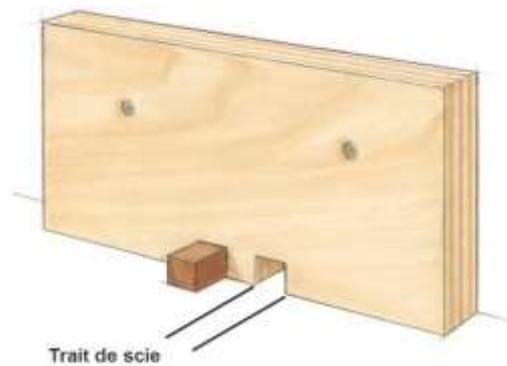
Le guide à coupe d'onglet et le guide à queues droites
